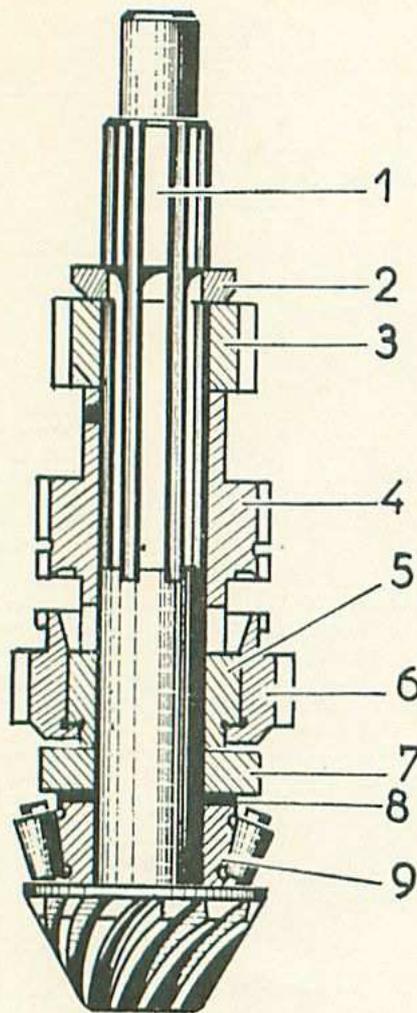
Vue en coupe des pièces empilées sur l'arbre pignon d'angle.
